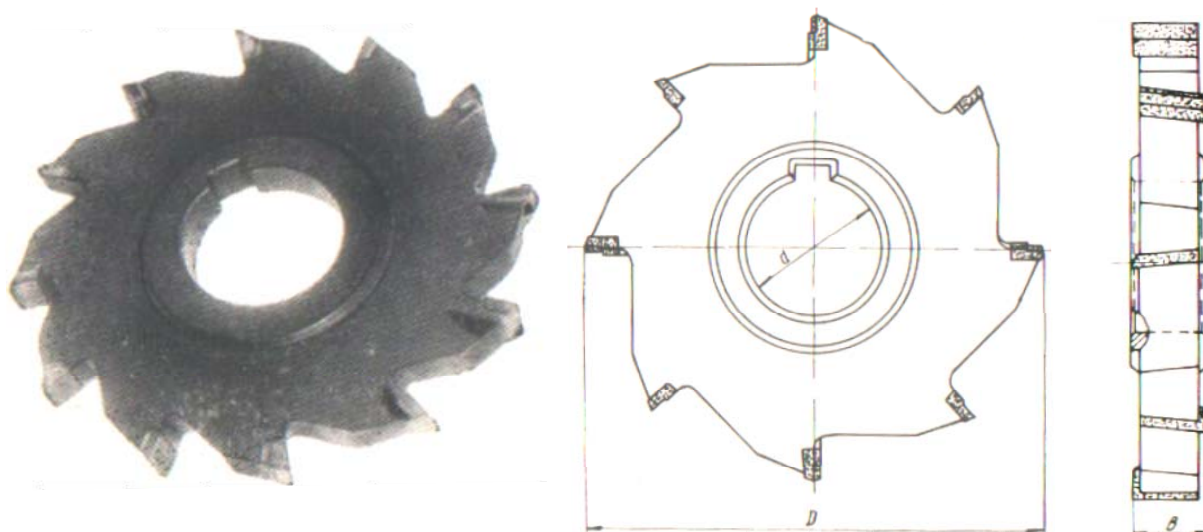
Дисковая фреза с напайными пластинами из быстрорежущей стали или твердого сплава
